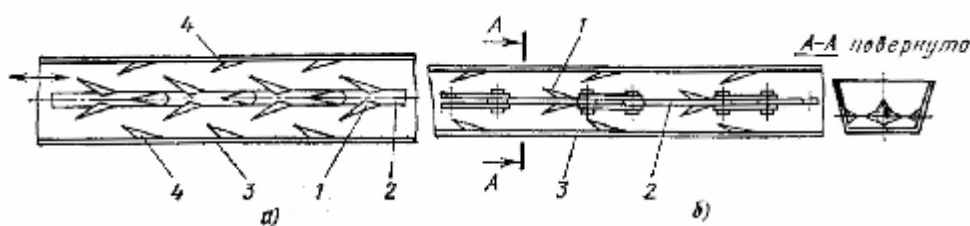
Ершово-штанговый (а) и цепной (б) конвейеры для удаления стружки.
